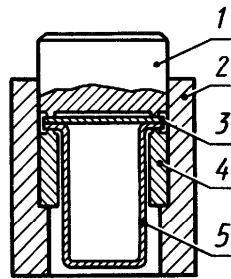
Схема сварки алюминиевых корпусов конденсаторов с крышками
